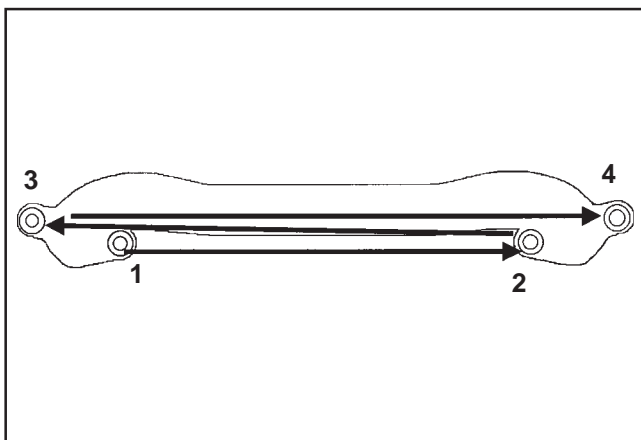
Sequenza di serraggio del collettore di aspirazione.
